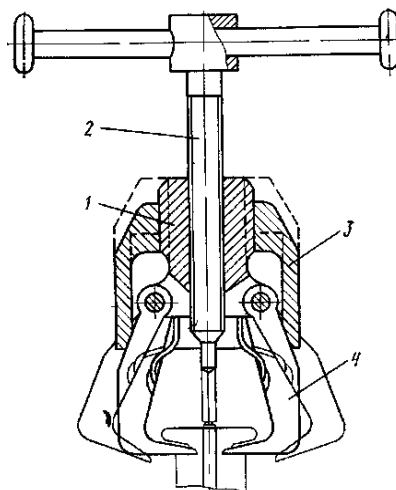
Знімач для знімання шестерні з кришки редуктора
